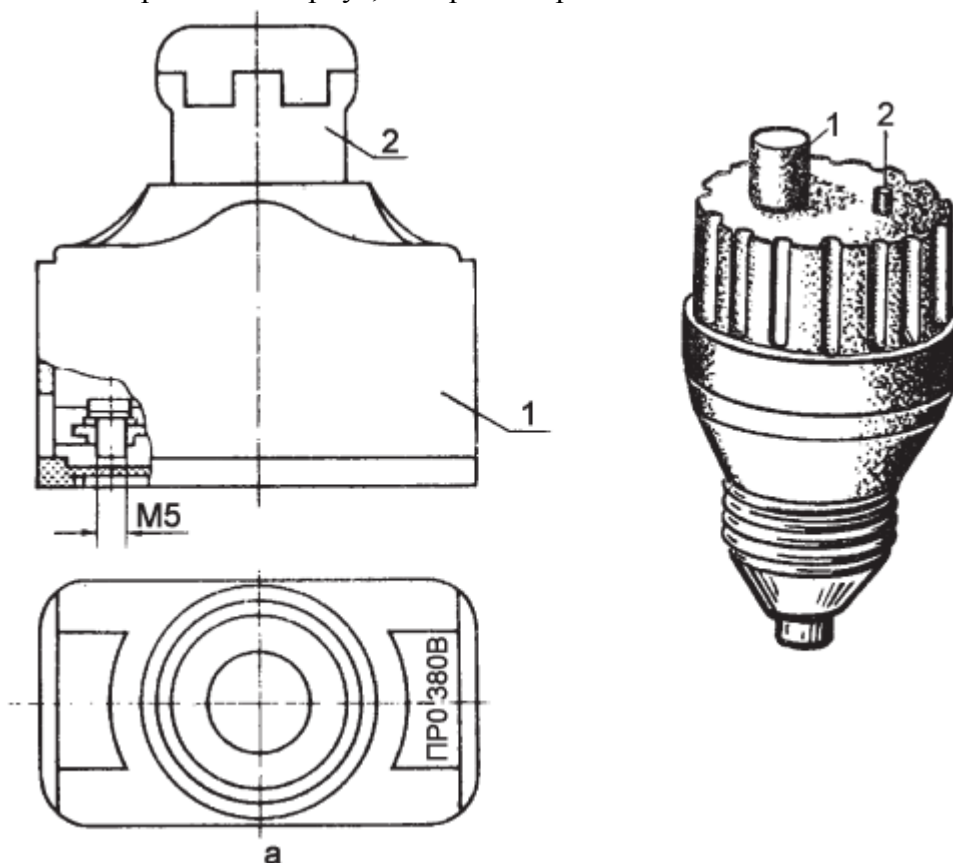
Аппараты электрозащиты: а – предохранитель серии ПРС: 1 – основание предохранителя; 2 – ввертываемый цилиндрический корпус с плавкой вставкой; б – автоматический выключатель ПАР-6,3 (ПАР-10): 1 – кнопка включения; 2 – кнопка отключения
